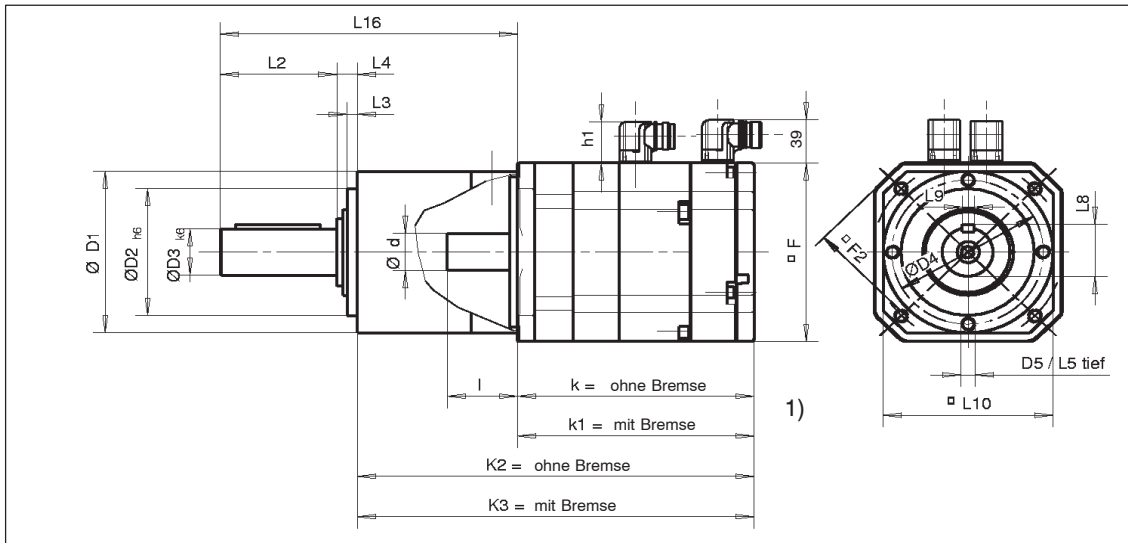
Maße 1FK6 Standard – Motor, AH 36 bis AH 80, mit Planetengetriebe
